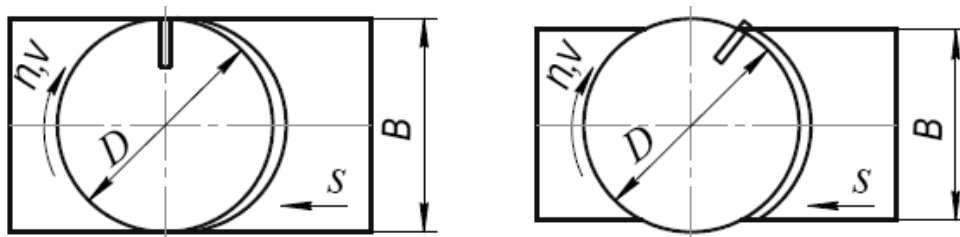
Вибір діаметра фрези при торцевому фрезеруванні
